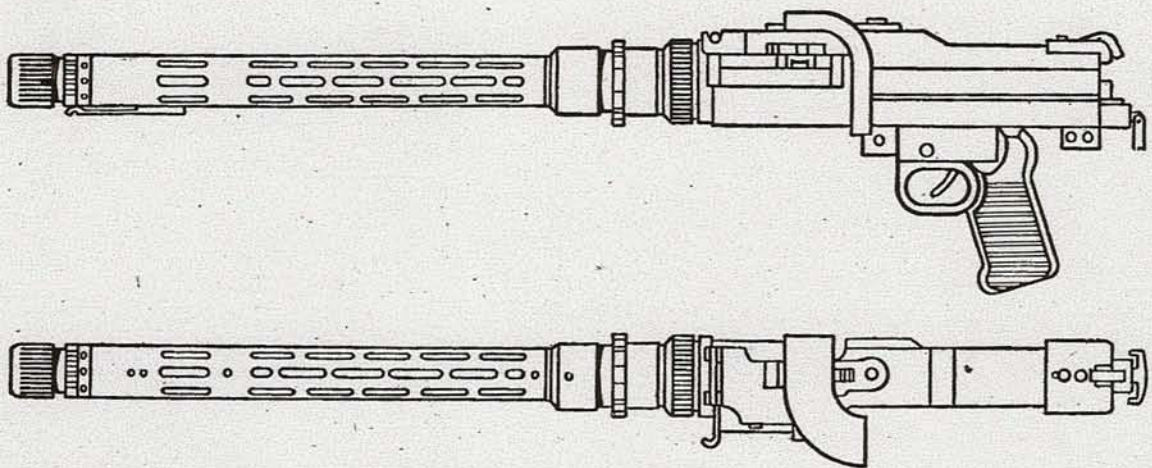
Maschinengewehr MG 81 (Kaliber 7,9 mm)
